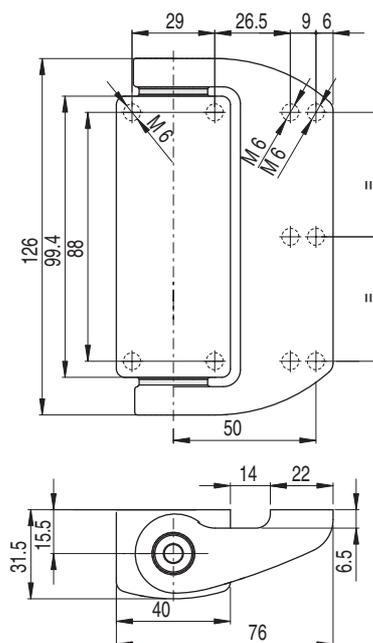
Dimensões da dobradiça adicional AC-H-S420 em mm
